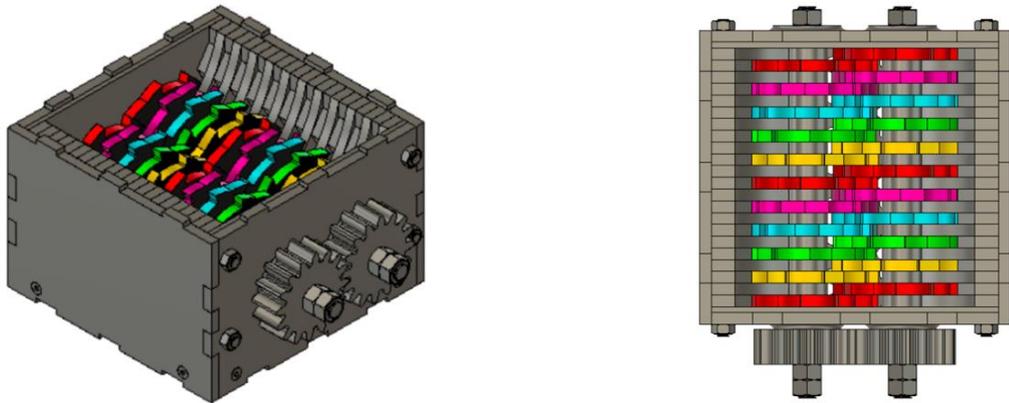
Caja previa en perspectiva y planta. Elaboración propia.
